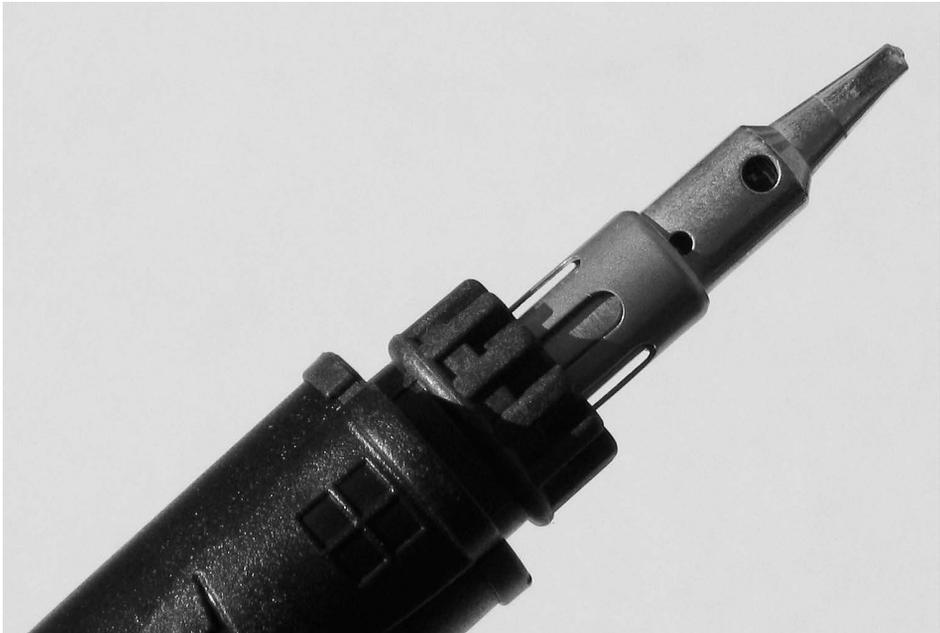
Lötspitze eines GaslötKolbens.
